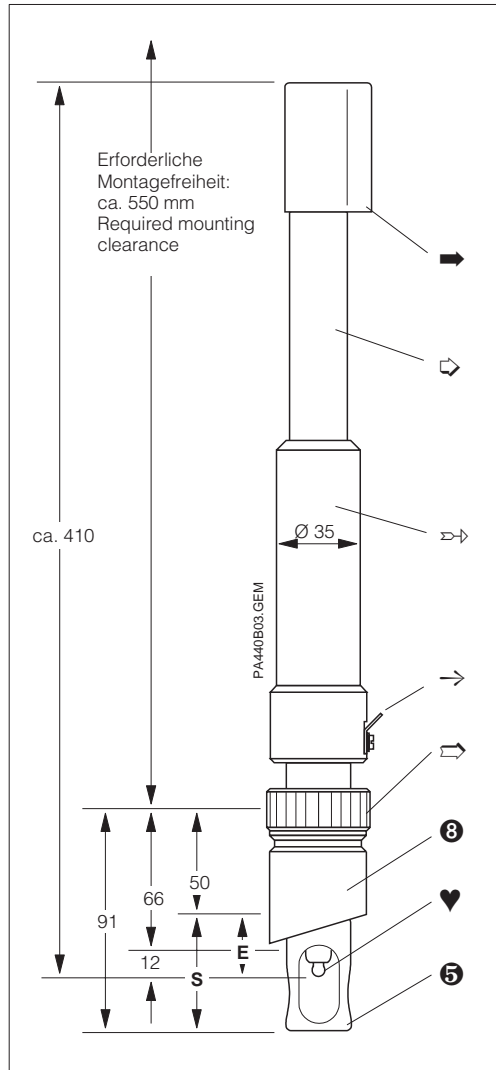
Maßzeichnung Profit CPA 440 mit Adapter DN 25
